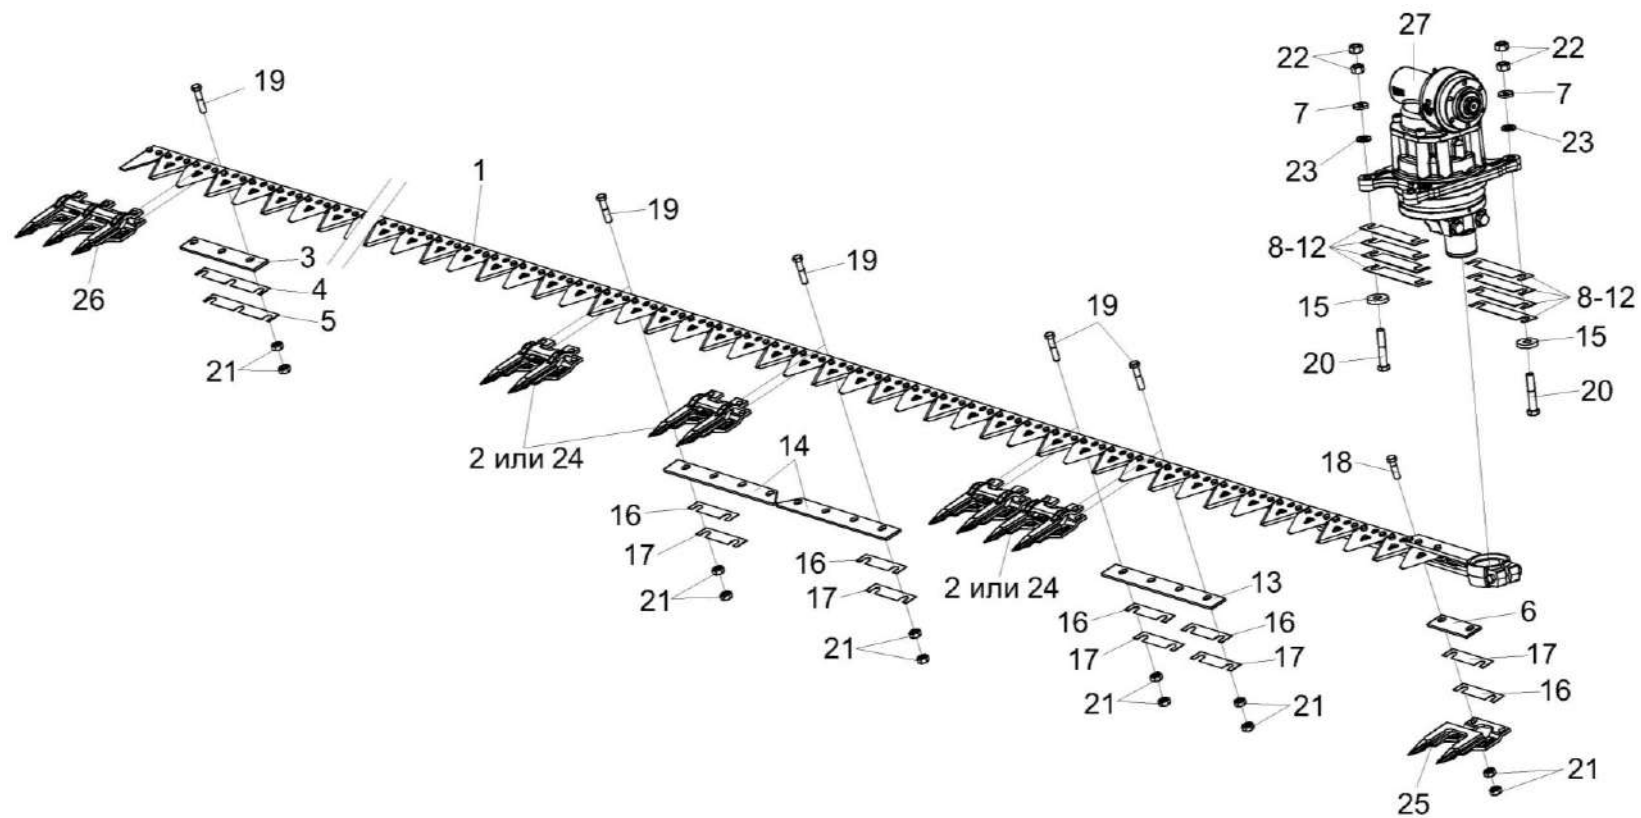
Установка аппарата режущего КЗК-1492-1507000А
